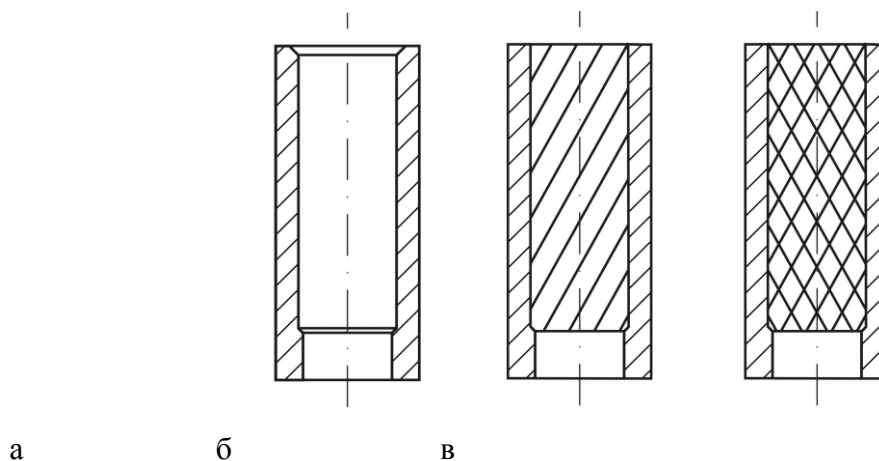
Схема получения канавок. а – заготовка; б – заготовка после первой операции; в – заготовка после второй операции.
